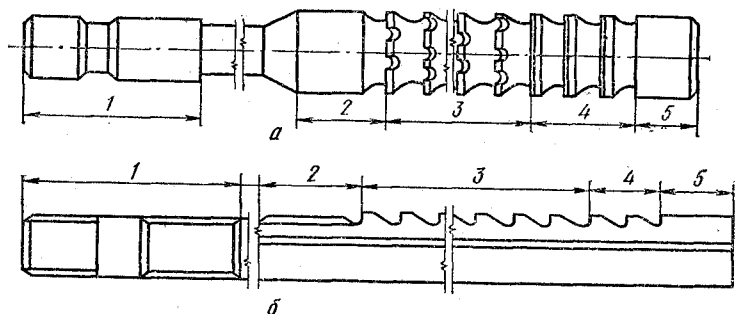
Конструкция цилиндрической (а) и шпоночной (б) протяжек
